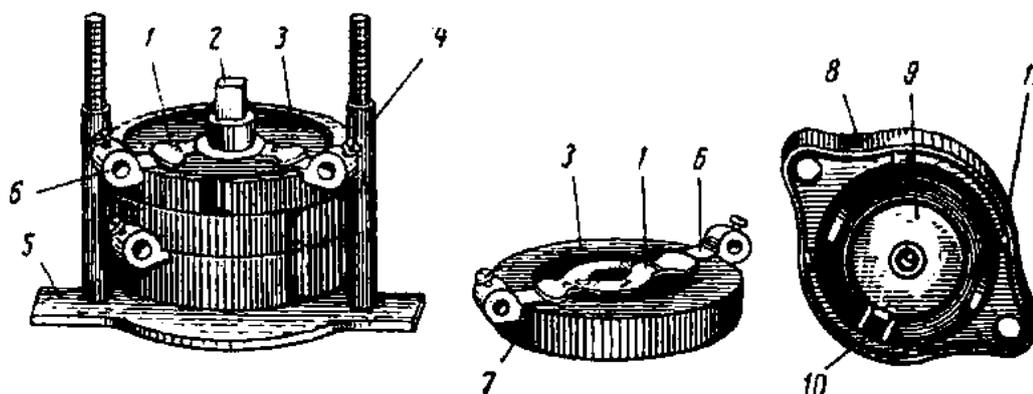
Пакетный выключатель: 1- подвижные контакты; 2 - валик; 3 - искрогасительная шайба; 4 - стяжная шпилька; 5 - скоба; 6 - неподвижные
